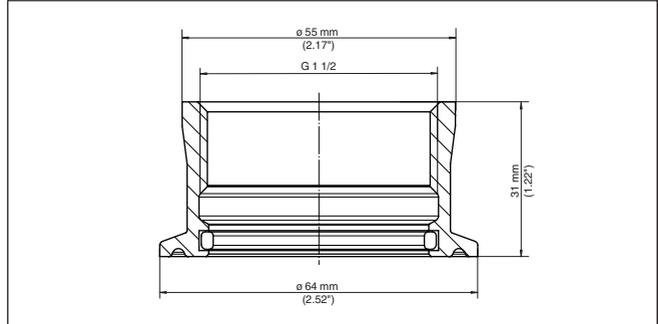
Dimensiones adaptador de rosca G1½ (DIN 3852-X) a Clamp 2" (DIN 32676, ISO 2852) PN 16
